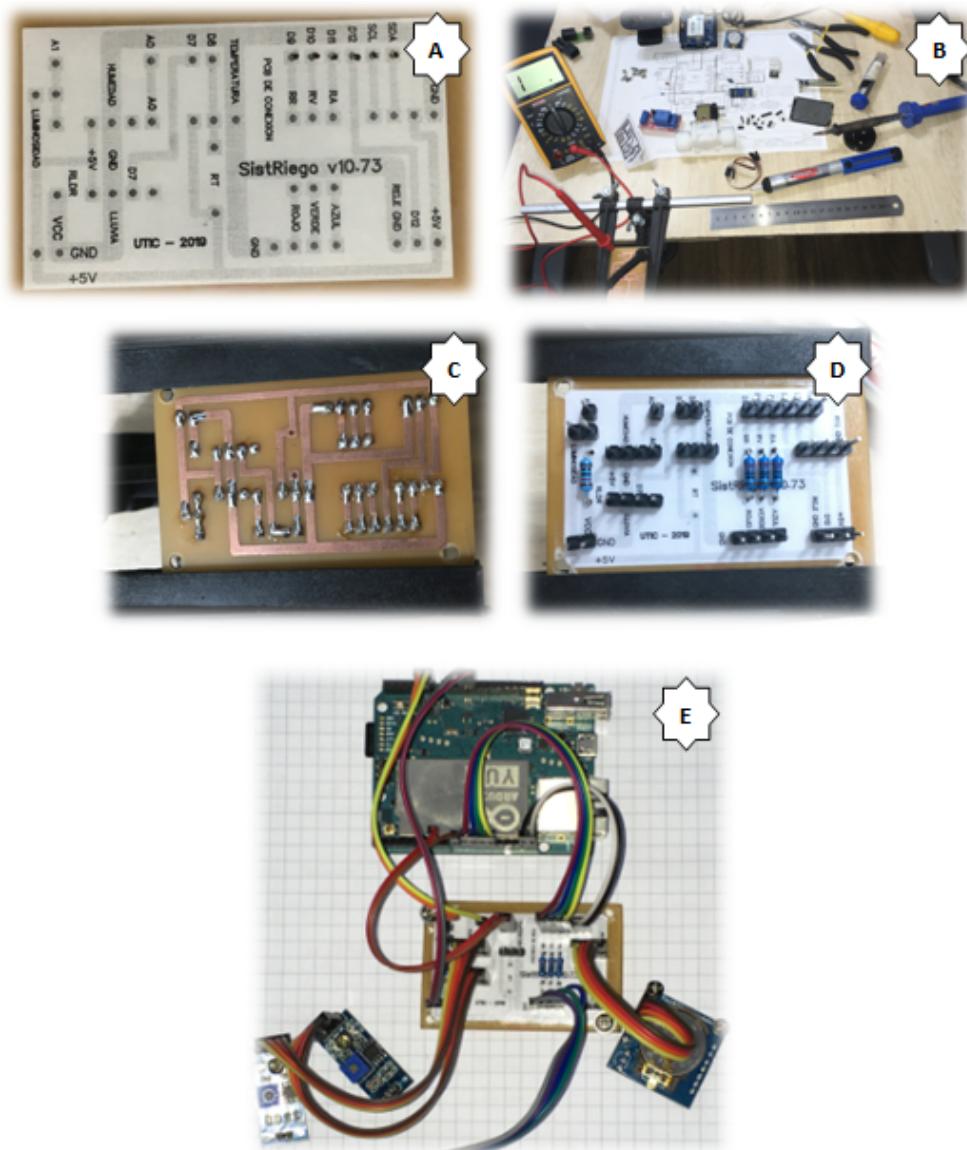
Proceso del PCB para el dispositivo. Fuente: Autor
